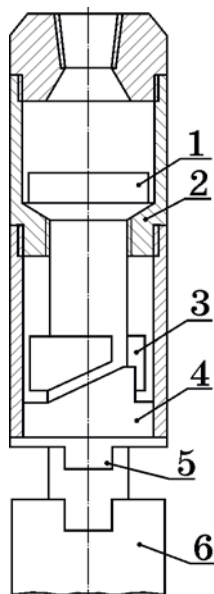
Вібратор глибинний механічний зубчастий конструкції Попова [107]
